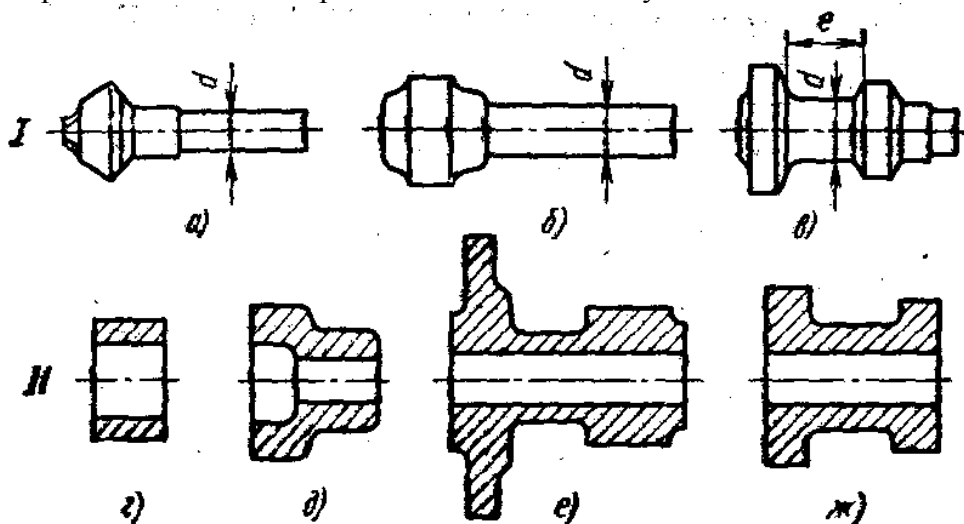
Заготовки зубчатых колес, штампуемых на ГКМ
